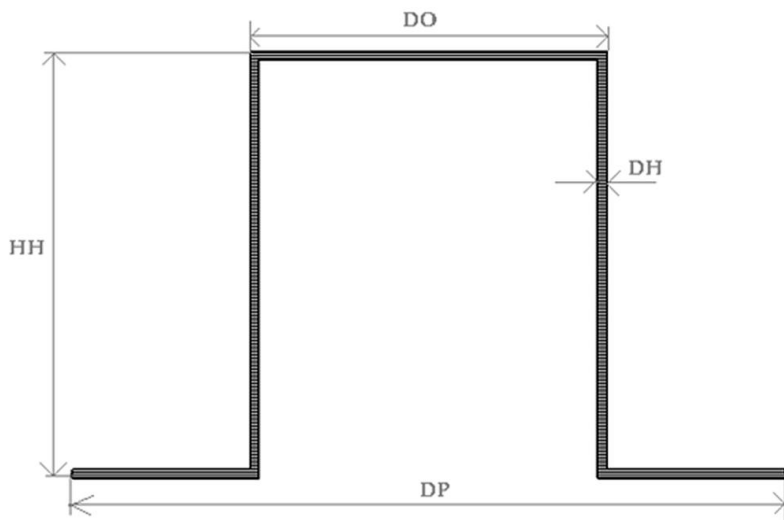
Вертикальный разрез шляпы типа цилиндр с указанием размеров
